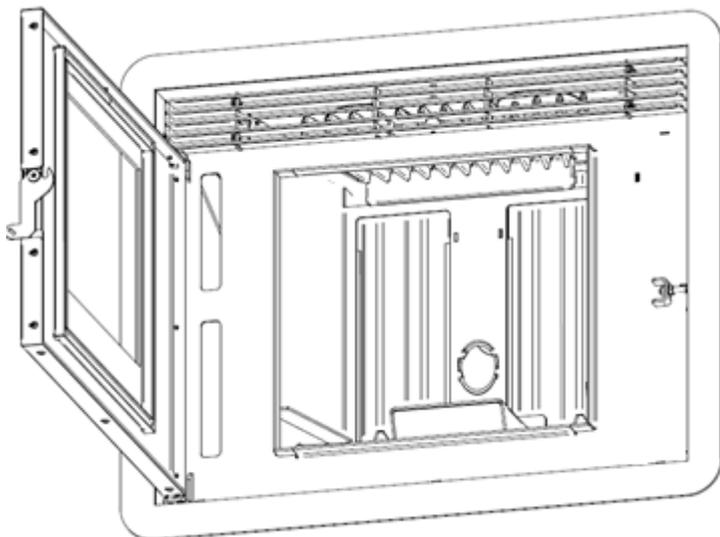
Vue d'ensemble de la chambre de combustion dépourvue des plaques de vermiculite.
